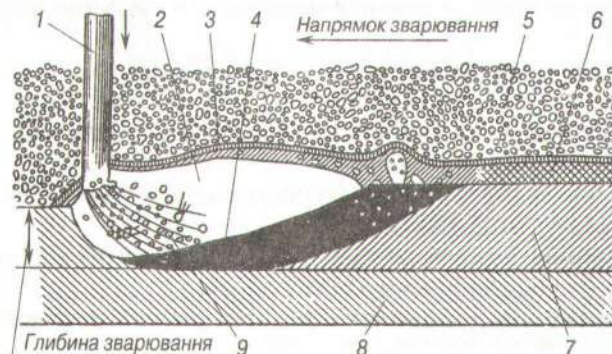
Схема горіння зварної дуги під флюсом:
